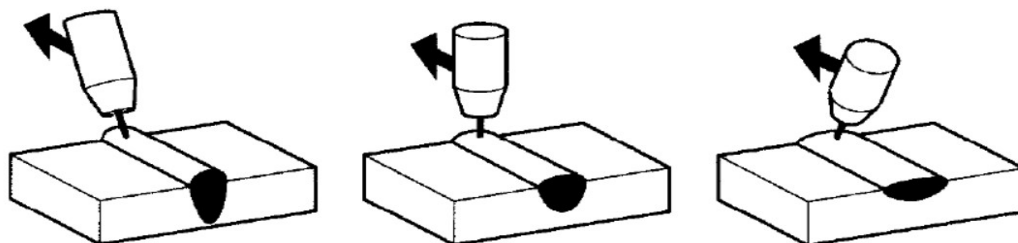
Efectos del cambio de ángulo del aporte en la geometría del cordón de soldadura (8).
